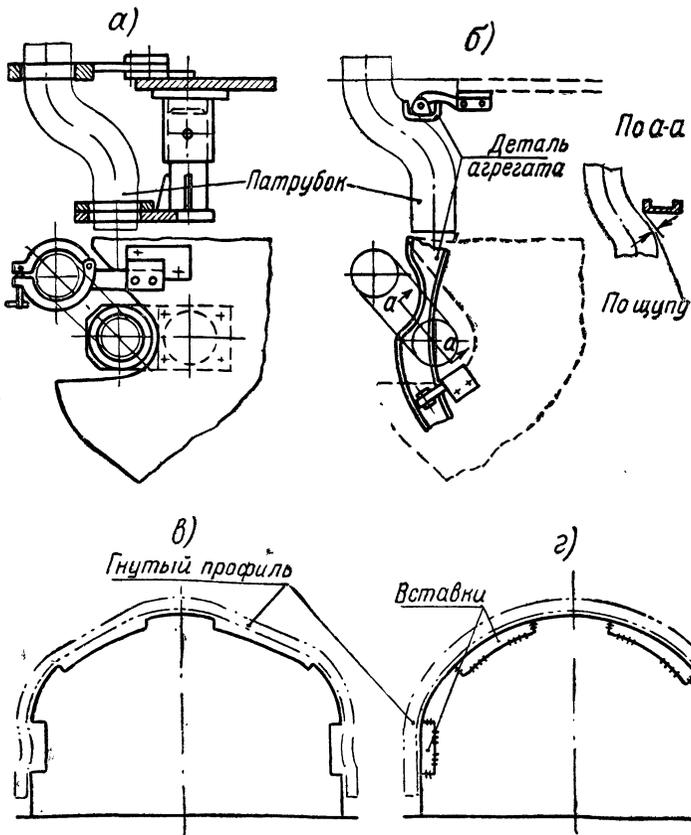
Изменение фиксаторов в связи с неувязками чертежей приспособлений.
